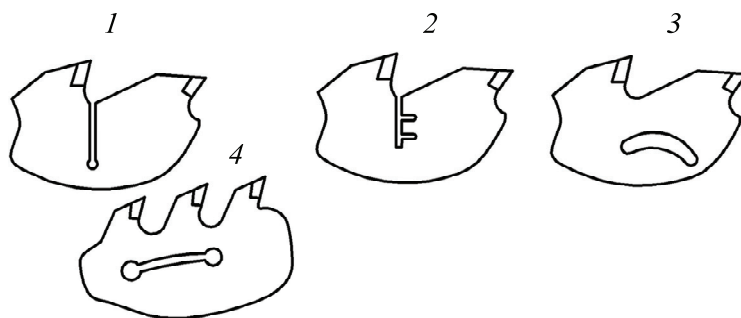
Формы прорезей в корпусах круглых пил с пластинами из твердого сплава
